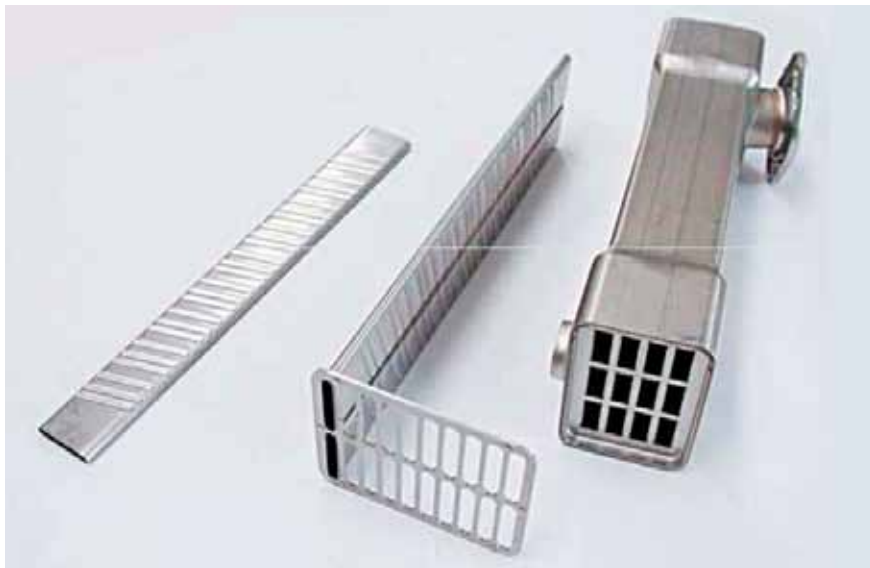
Lasersvetsning av komponenten som styr gasströmmen i värmeväxlaren sker i sex svetsstationer med CO₂-laser. Delar av komponenten kommer att svetsas med disk- eller fiberlaser i framtiden. Källa: Weil Engineering GmbH
